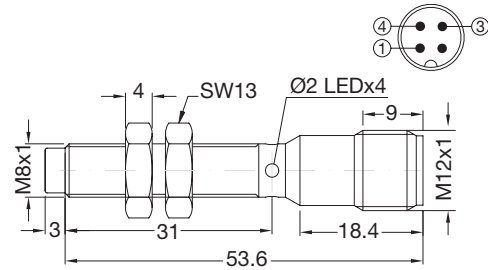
Kurze Ausführung, Nicht bündiger Einbau, M12 Steckversion
